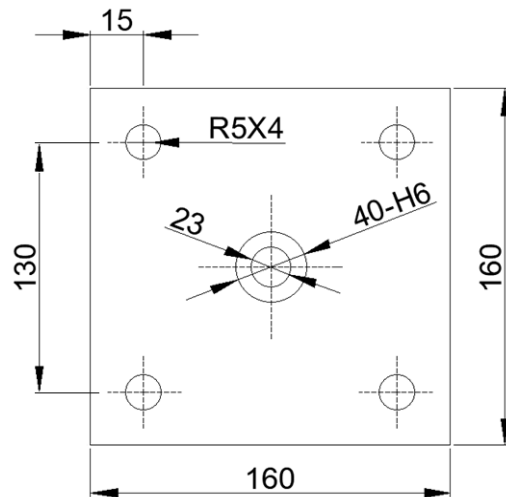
Dimensiones en mm de la placa superior móvil con la que cuenta la máquina de ensayos de tracción [23].
